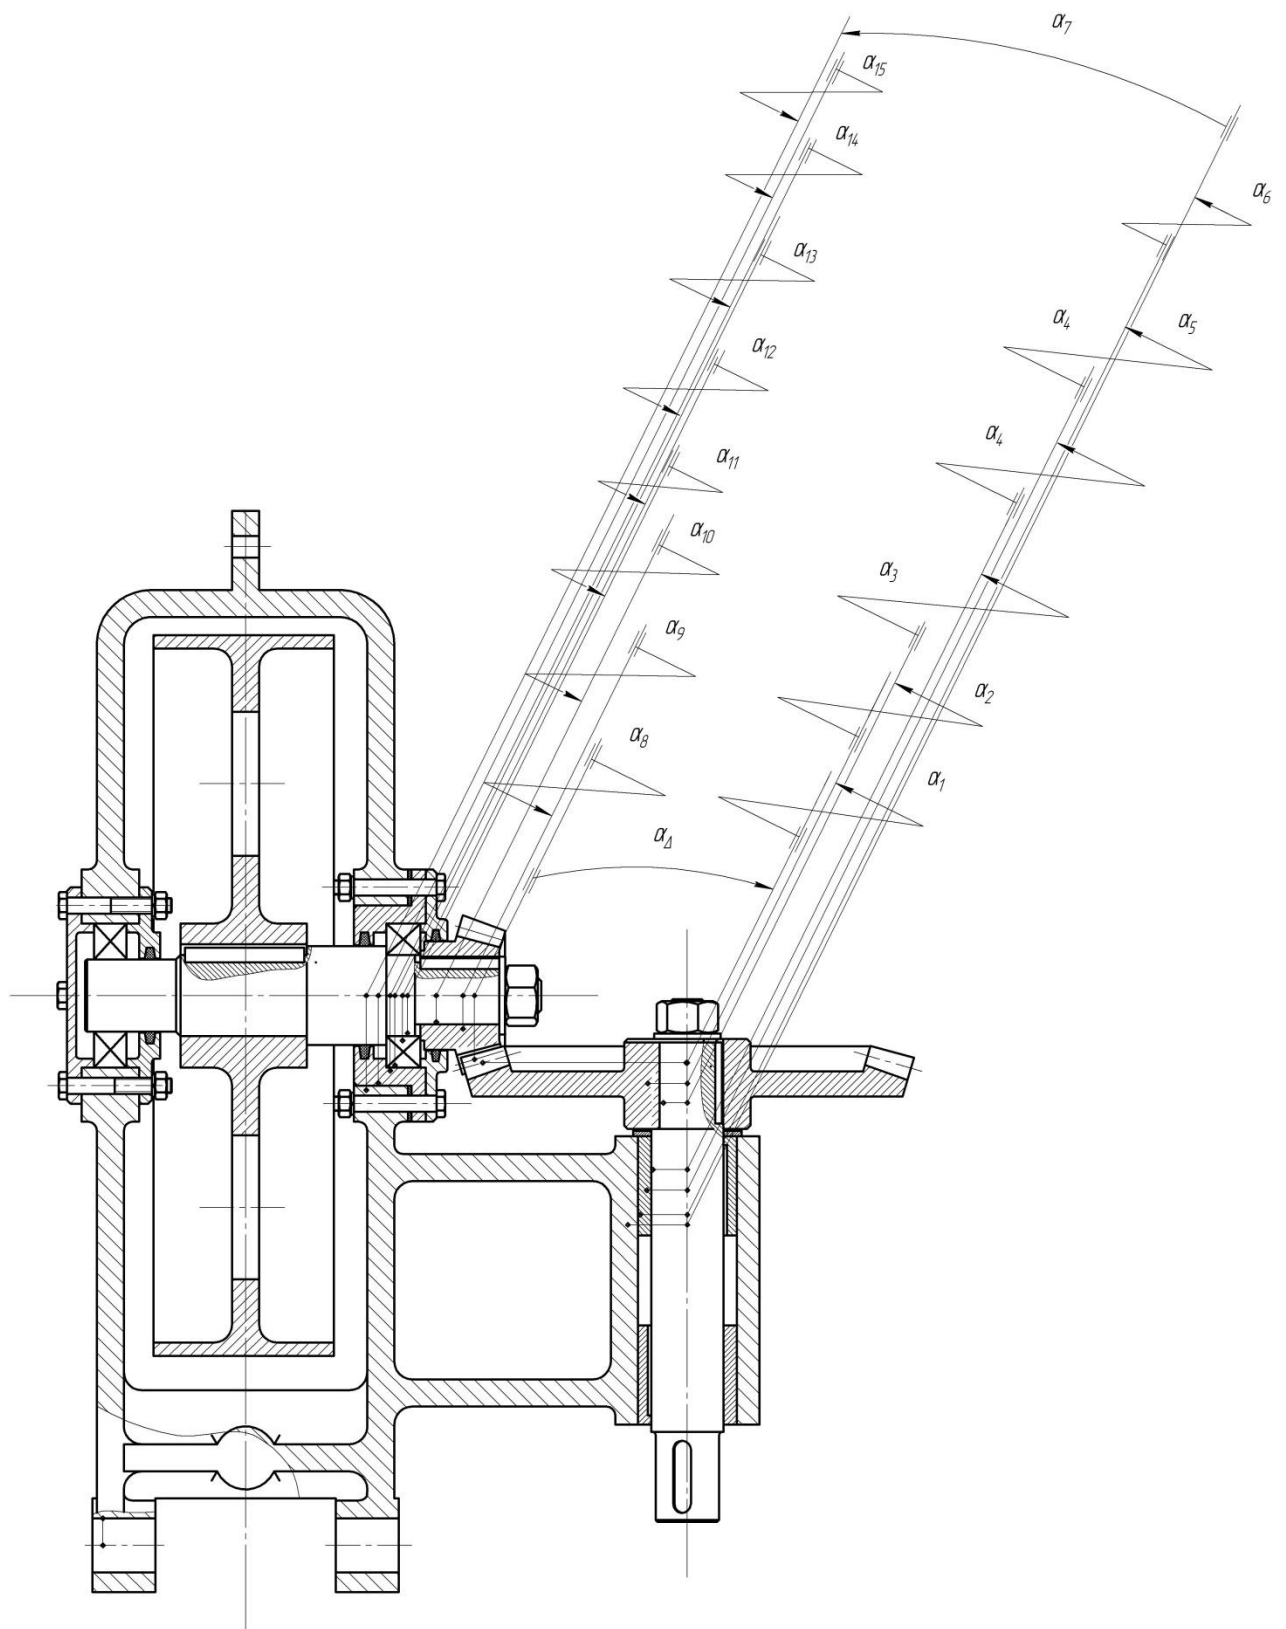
Розмірний ланцюг, який забезпечує точність кутового розташування зубчастих коліс
